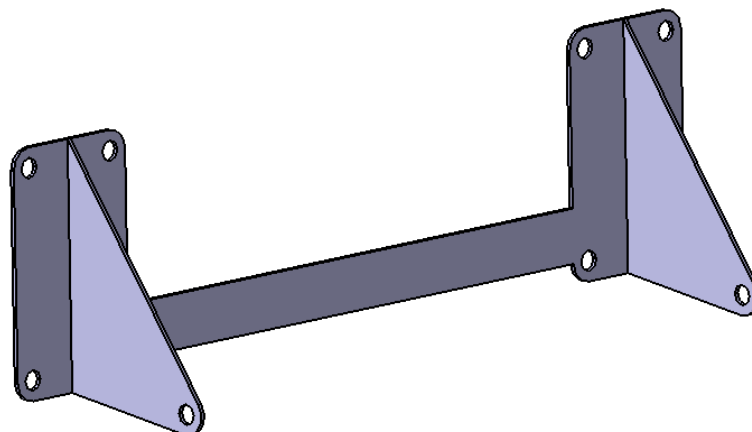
Shoulder belt seat roller* 11: Resultado de soldadura
